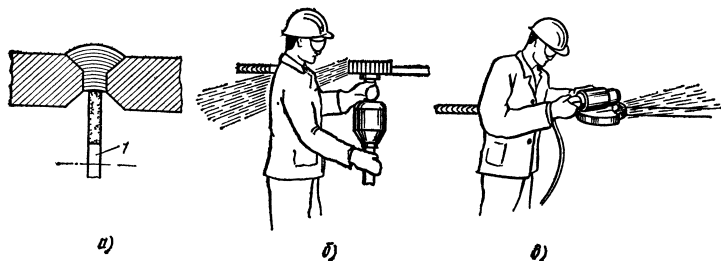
Схемы зачистки корня сварного шва:
